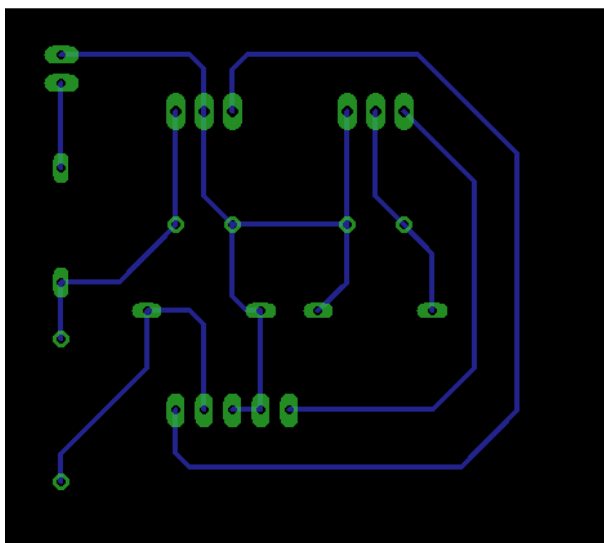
5ª fase desarrollo PCB: circuito impreso final
